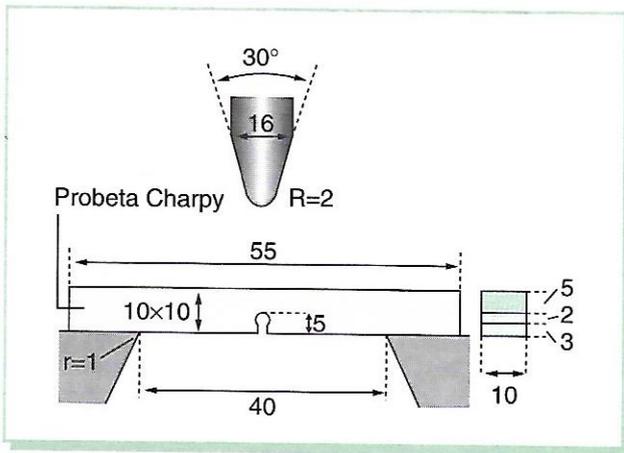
Dimensiones de la cabeza del martillo, del soporte y de la probeta del ensayo Charpy.
